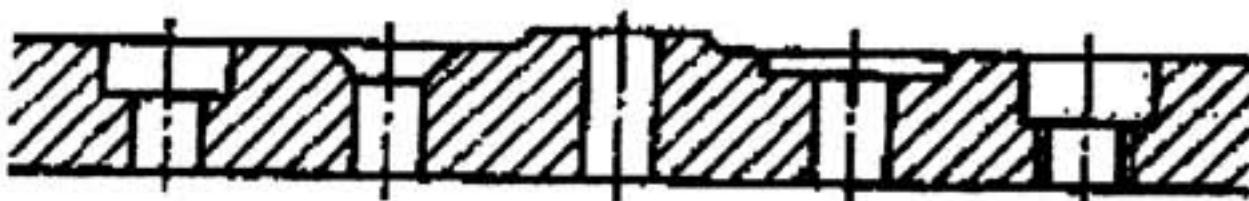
Отверстия, обрабатываемые ступенчатыми сверлами
